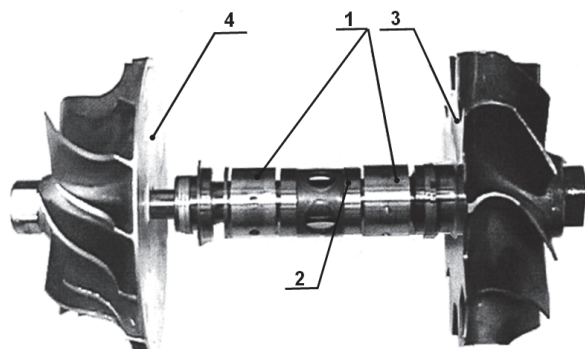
Ротор турбокомпрессора ТКР-8,5С: 1 – плавающие втулки; 2 – дистанционная втулка; 3 – колесо турбины; 4 – колесо компрессора
